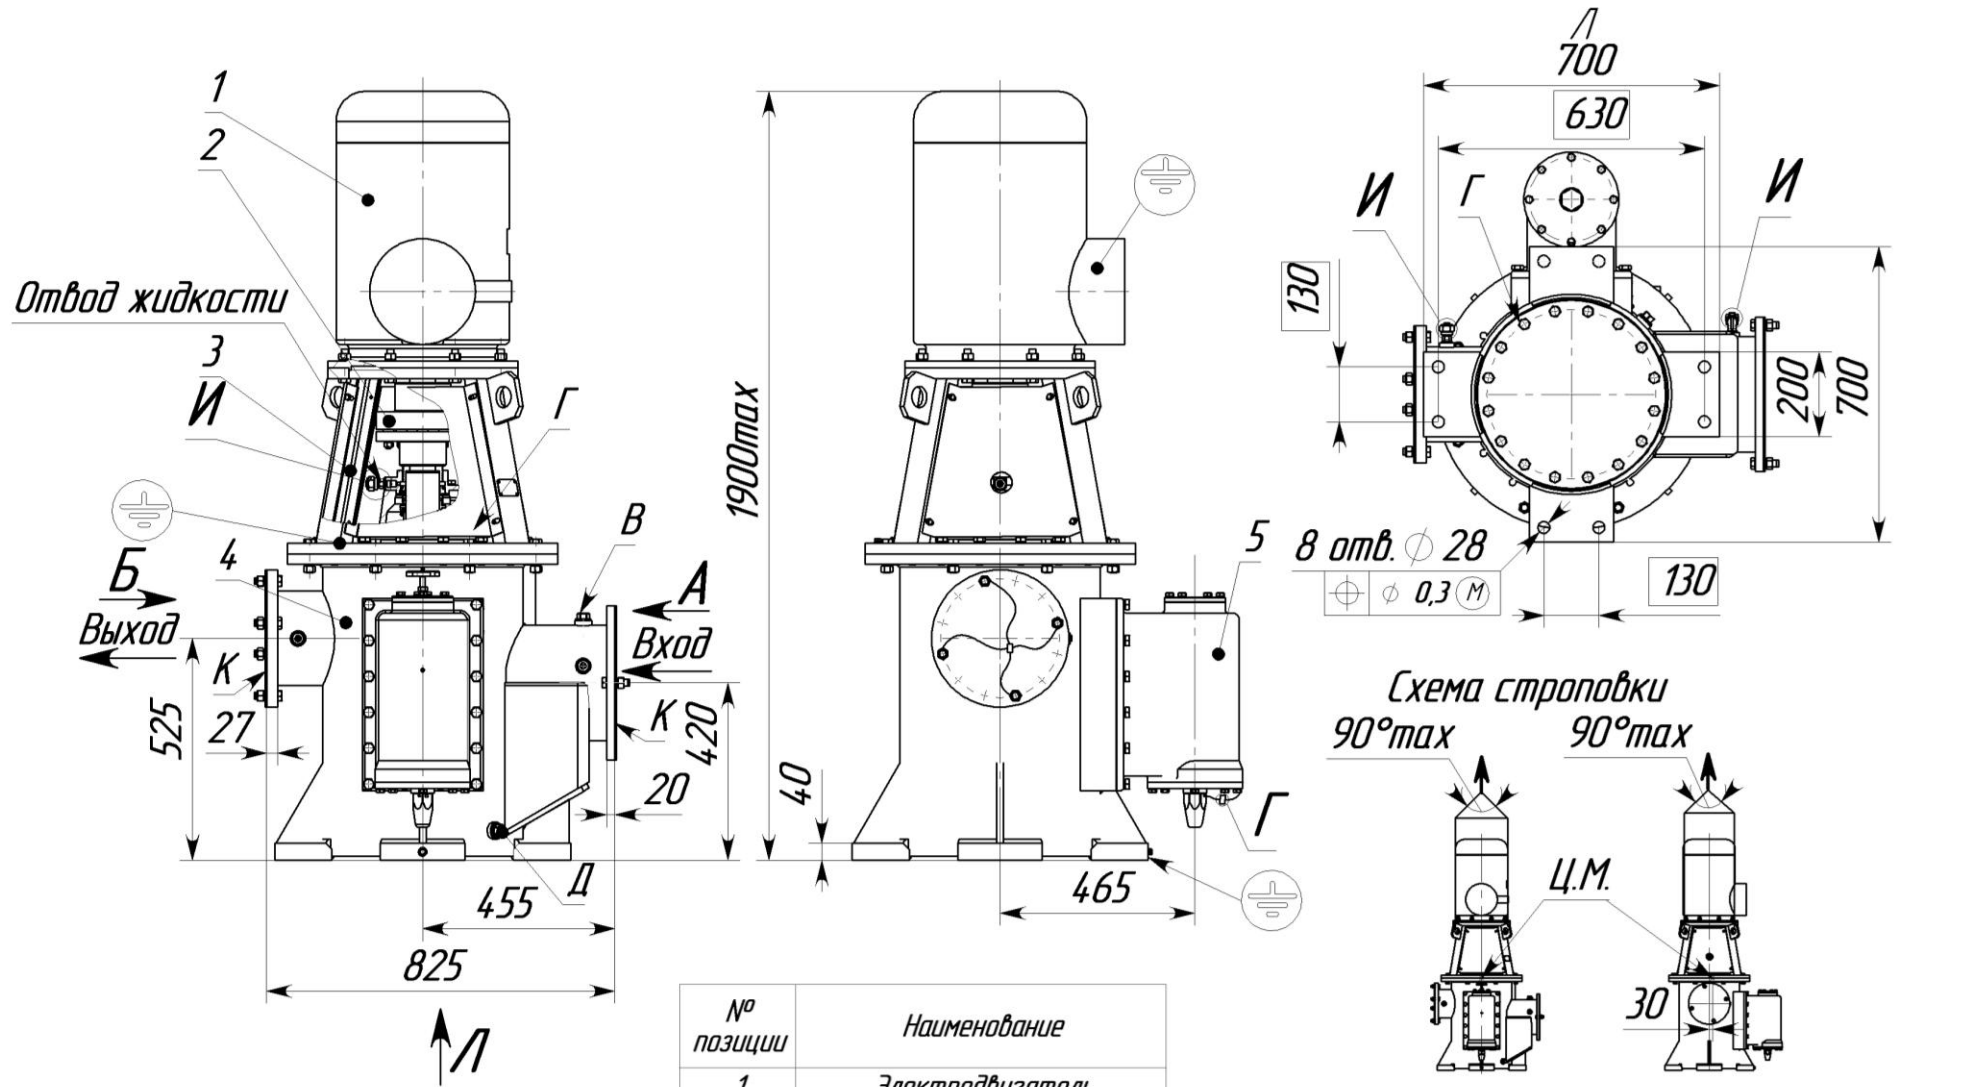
Габаритный чертеж насоса типа А1 3В 400/16
